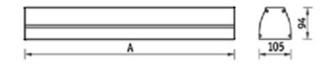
Габаритные размеры светильника с крышками для одиночной установки
